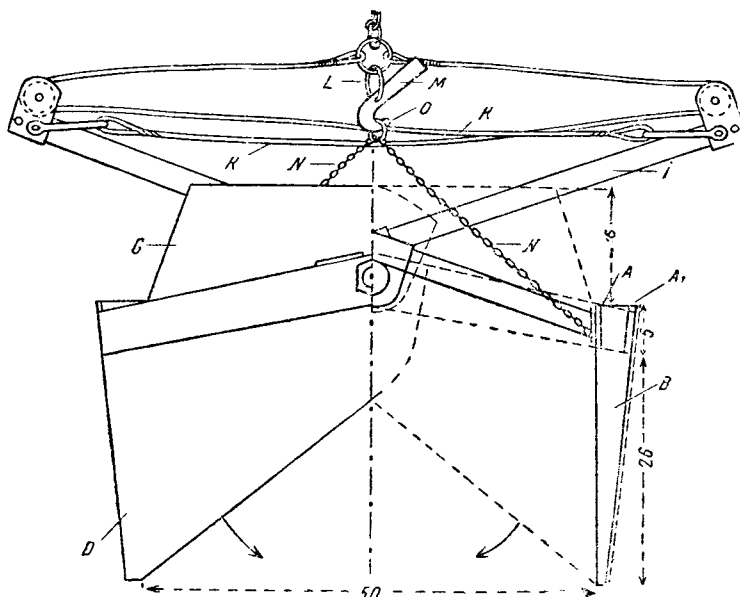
Зубчатый дночерпатель В. Д. Гордеева
